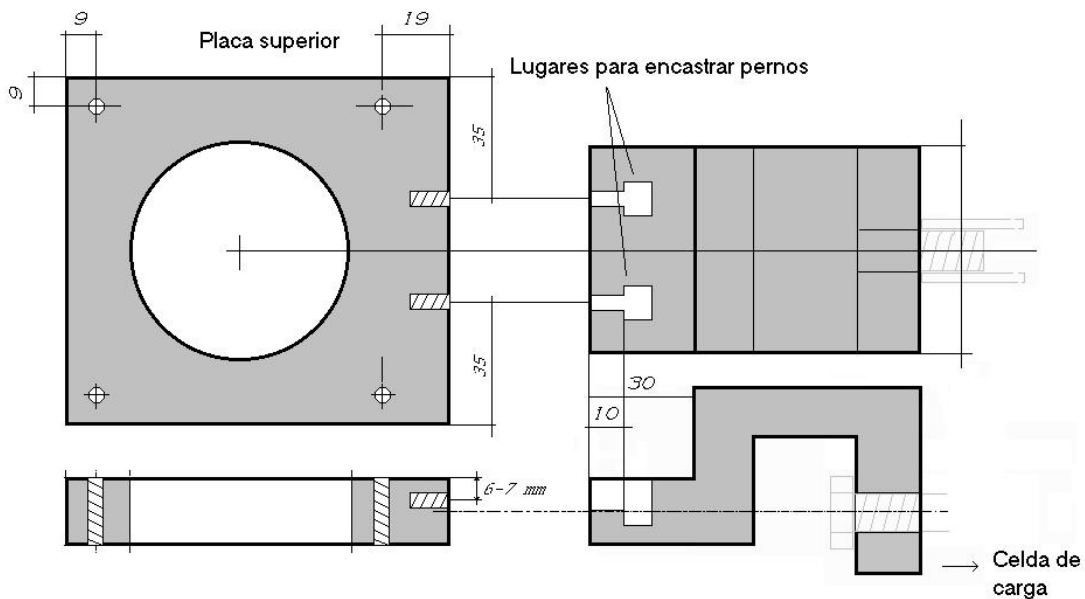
Sección en planta de la caja de corte (arriba) y vertical (abajo)
